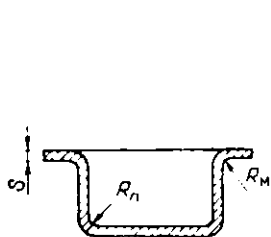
Радиусы сопряжения полый цилиндрической детали
